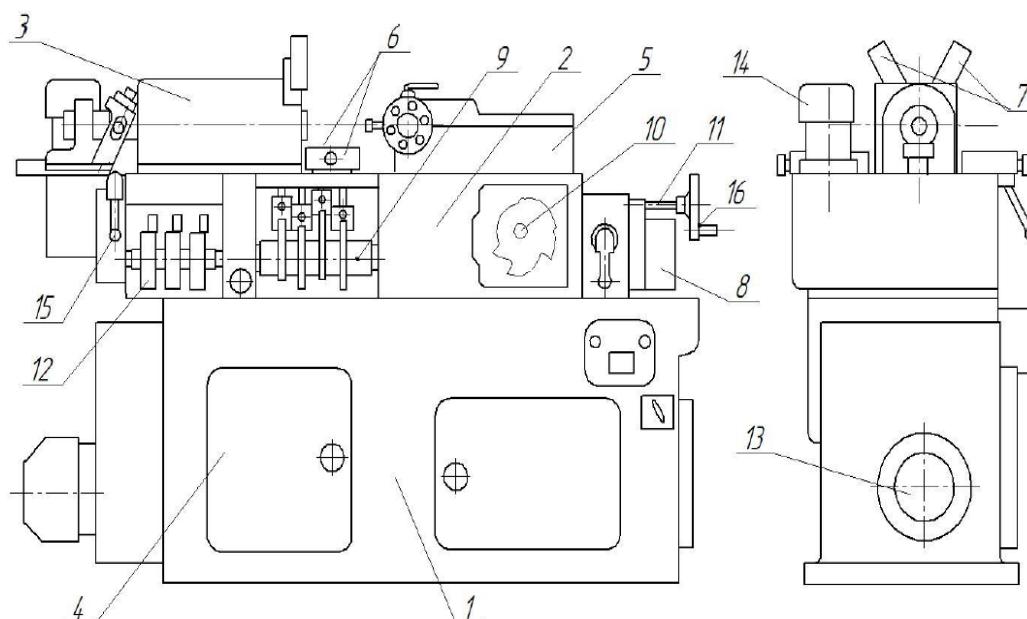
Основні вузли верстата 1Б140: 1 – основа; 2 – станина; 3 – шпindelна бабка; 4 – коробка швидкостей; 5 – револьверний супорт; 6 – поперечні супорти (передній, задній); 7 – вертикальний супорт (задній, передній); 8 – масляний лоток; 9 – розподільний вал поперечних супортів; 10 – розподільний вал револьверного супорта; 11 – допоміжний вал; 12 – барабани керування; 13 – двигун привода головного руху; 14 – двигун привода розподільного вала; 15 – головний важіль керування; 16 – маховик допоміжного вала
